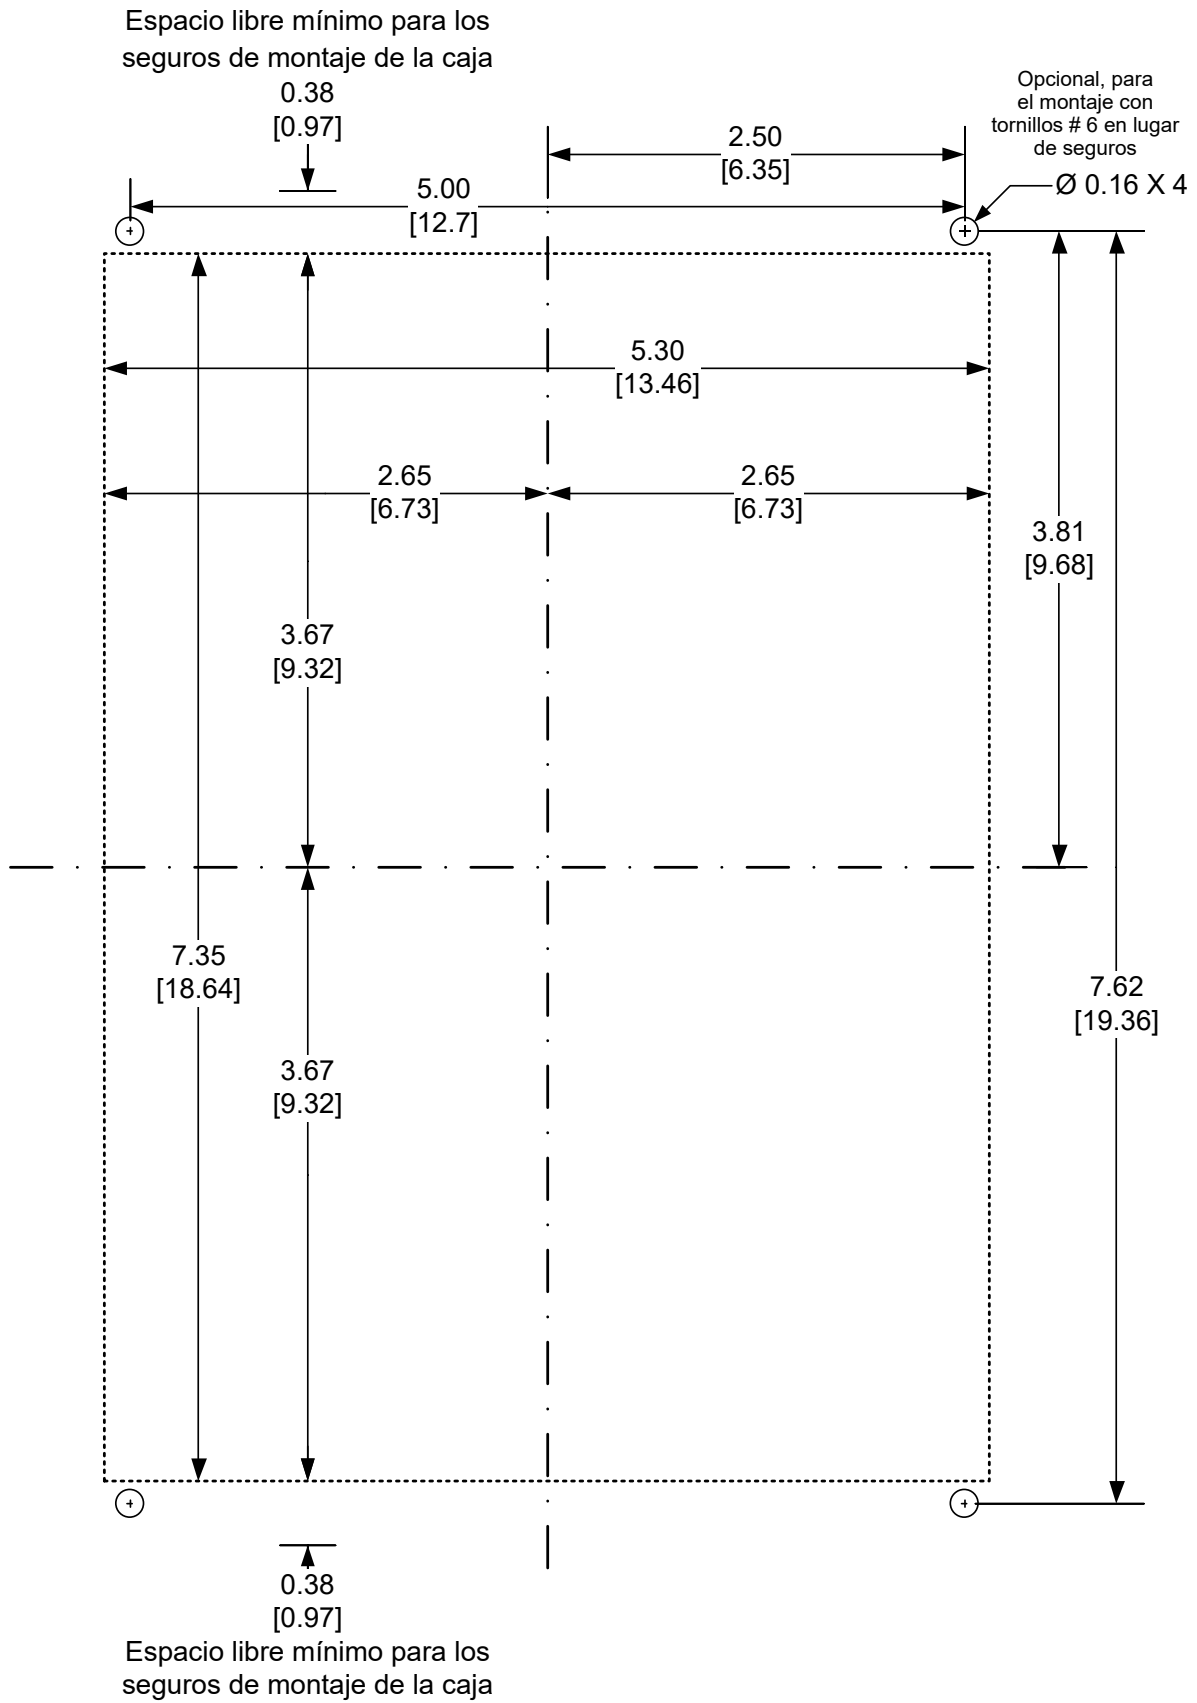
M-7679 Dimensiones de Corte del Panel Vertical
